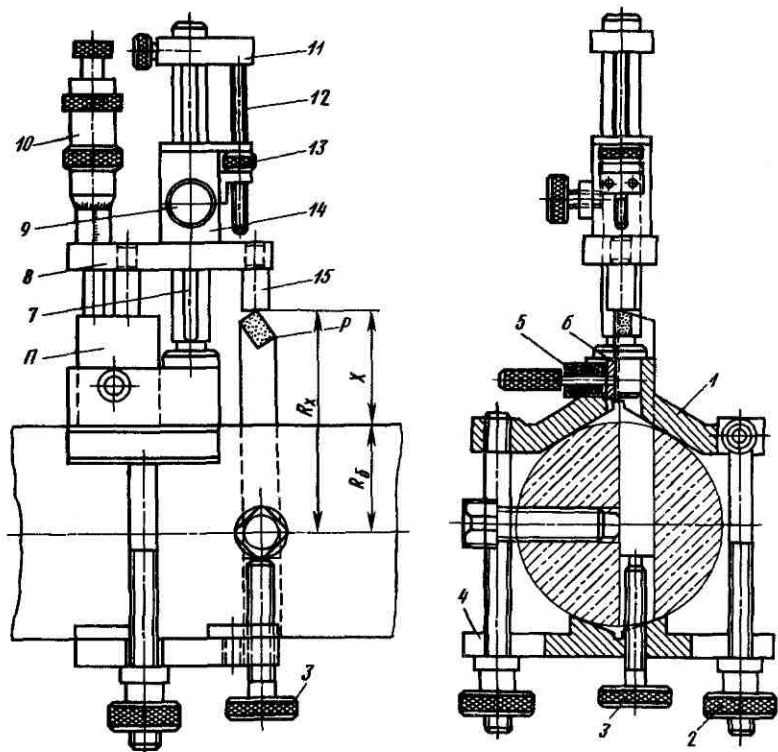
Универсальное приспособление для установки инструмента в борштанге
